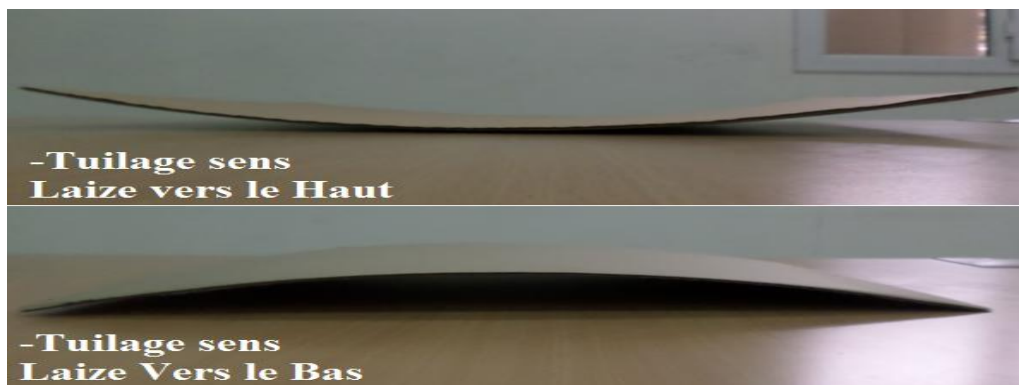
Tuilage de la plaque du CO Sens Laize
